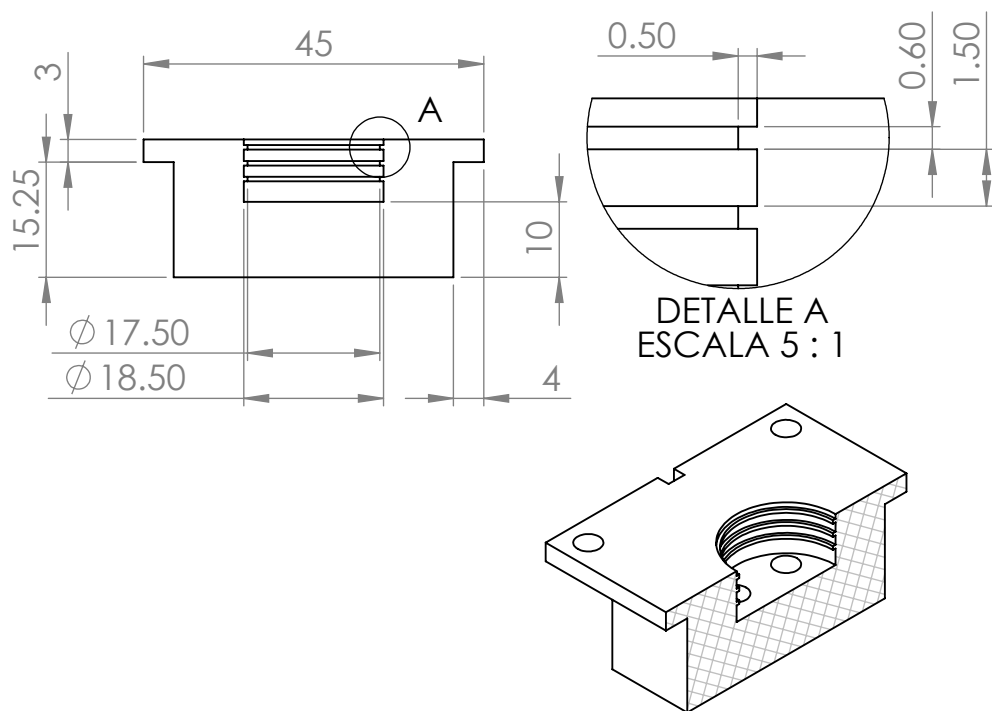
Vista en corte del molde del *Robot Uniaxial* parte B
